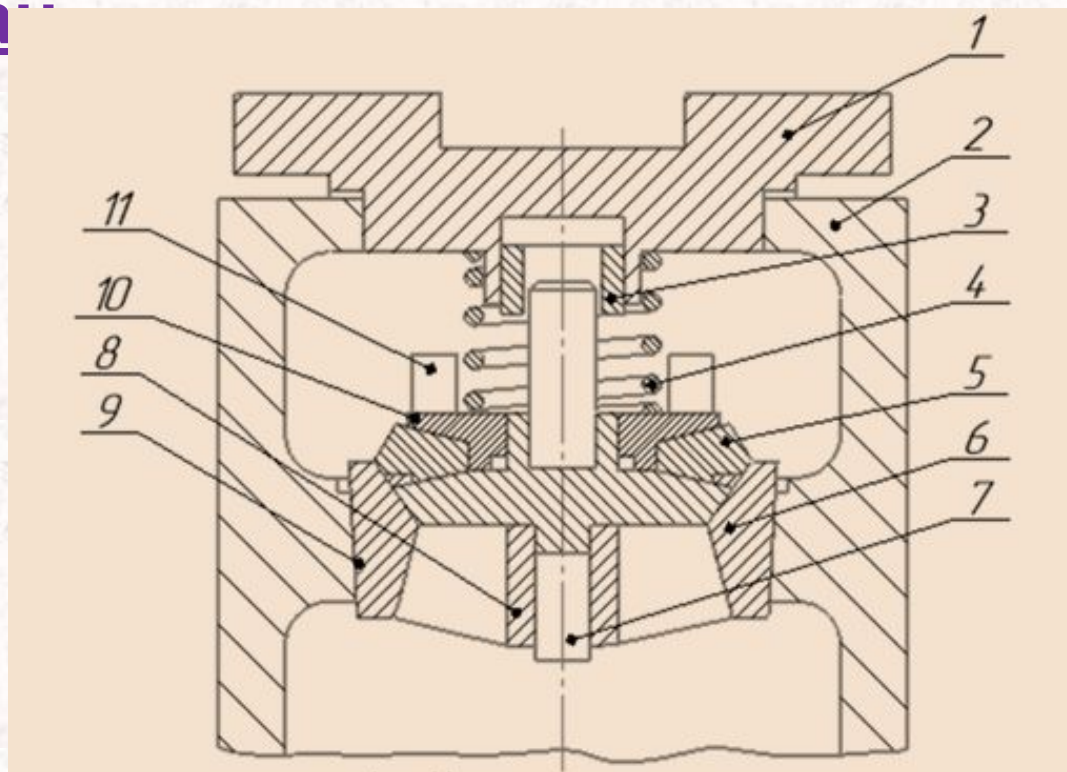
Насосный клапан (1 – крышка; 2 – структурная стенка; 3 – направляющая втулка; 4 – пружина; 5 – уплотнительный элемент; 6 – седло; 7 – шток; 8 – направляющий элемент; 9 – круглый канал; 10 – опорный стержень; 11 – молоточковые выступы)
